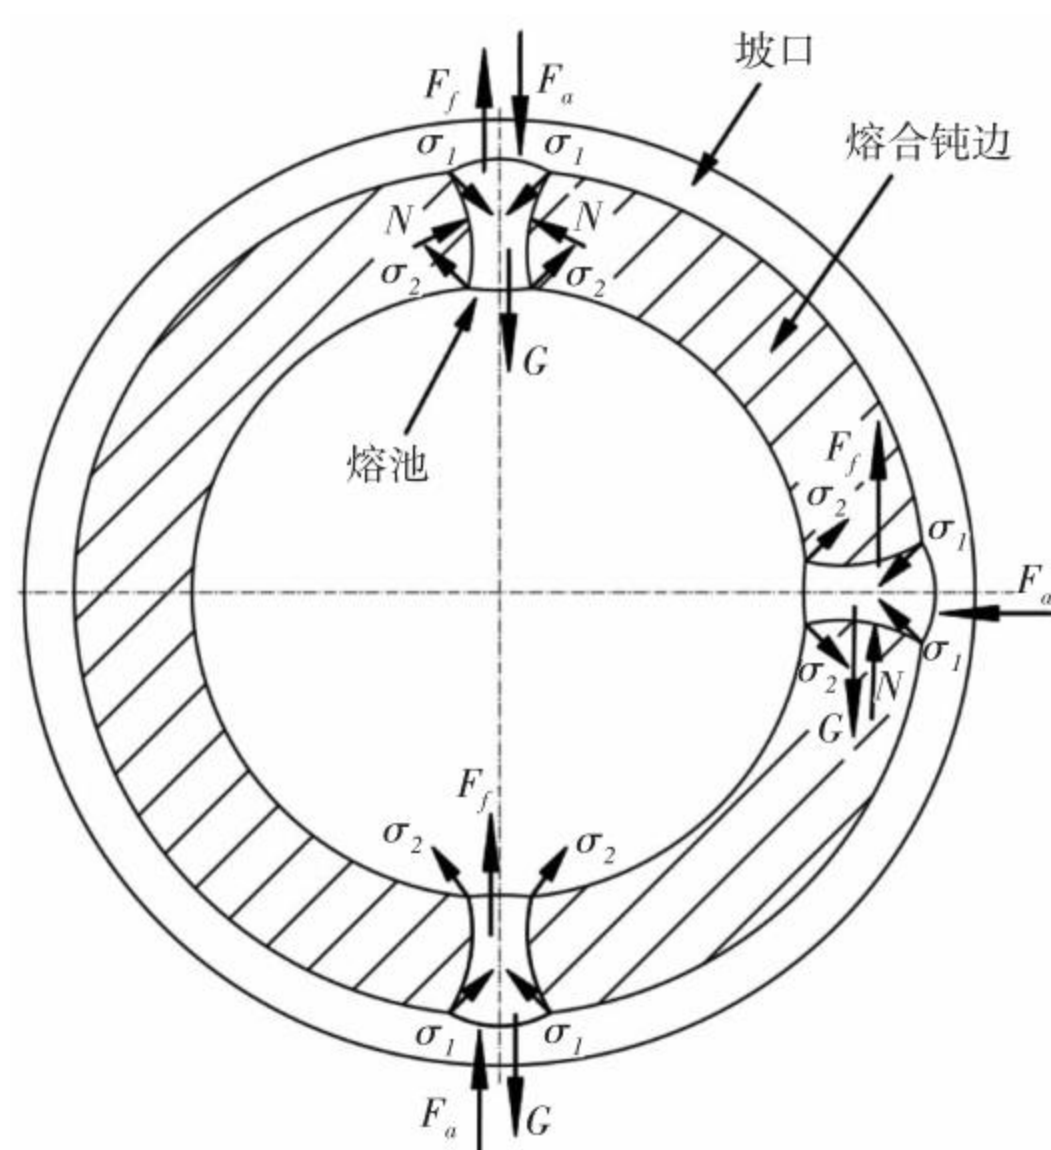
A-TIG 全位置打底焊熔池受力分析
